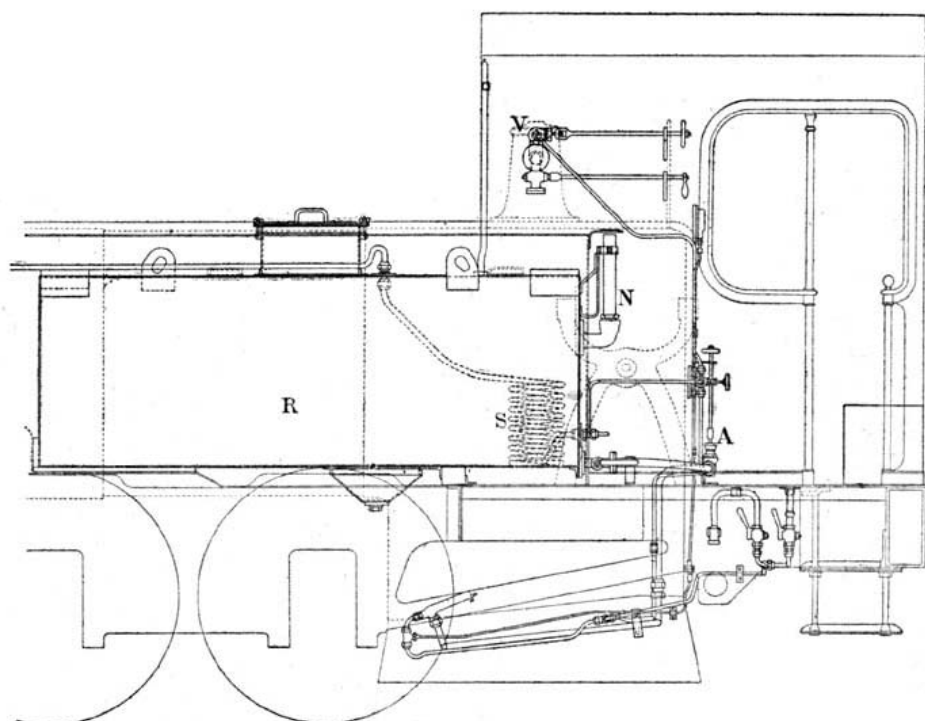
Conjunto de instalación para calefacción a combustible líquido sobre una locomotora-ténder P.L.M.
